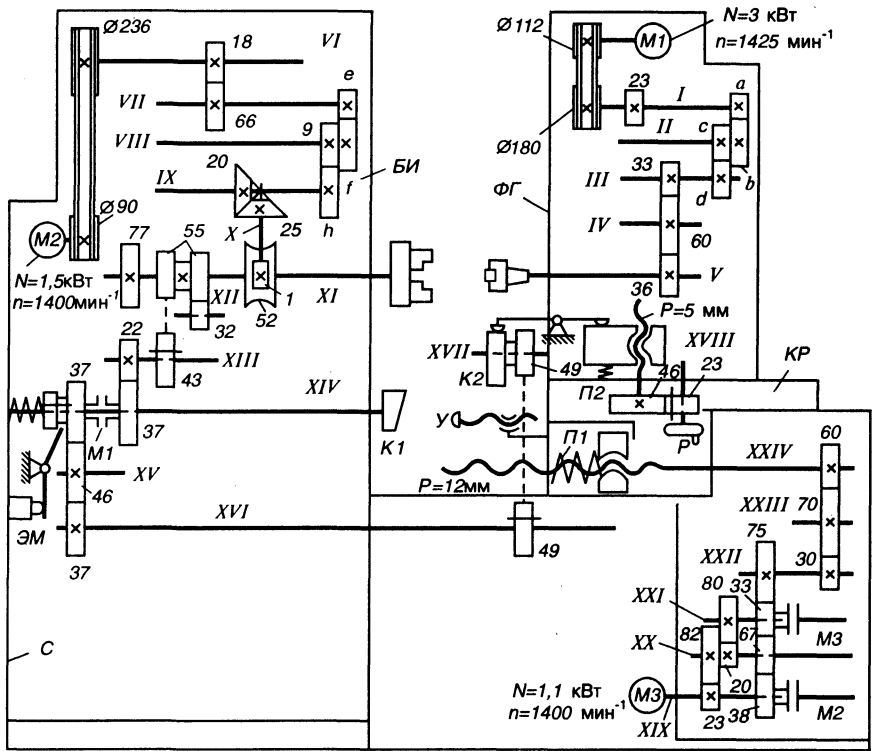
Кинематическая схема резьбофрезерного полуавтомата 5Б63
